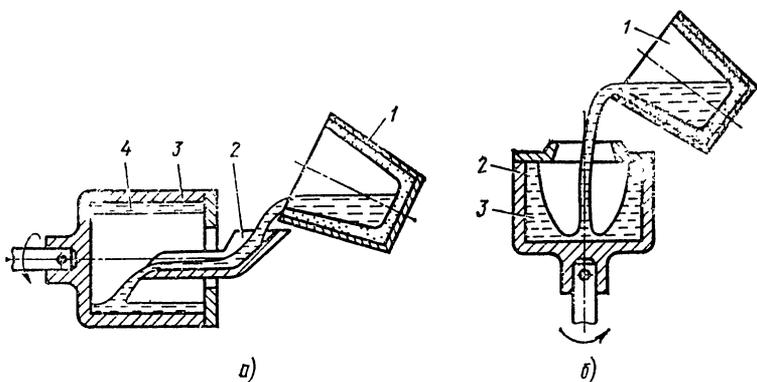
Схемы изготовления отливок на центробежных машинах с осью вращения:
